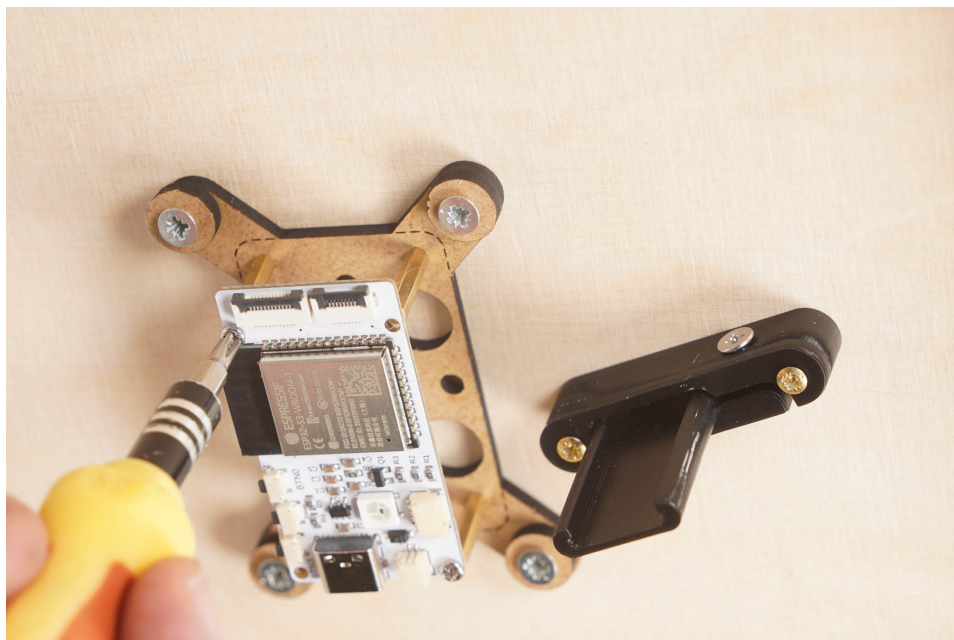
Der Controller wird mit einer kleinen Schraube auf einem der Abstandshalter befestigt
